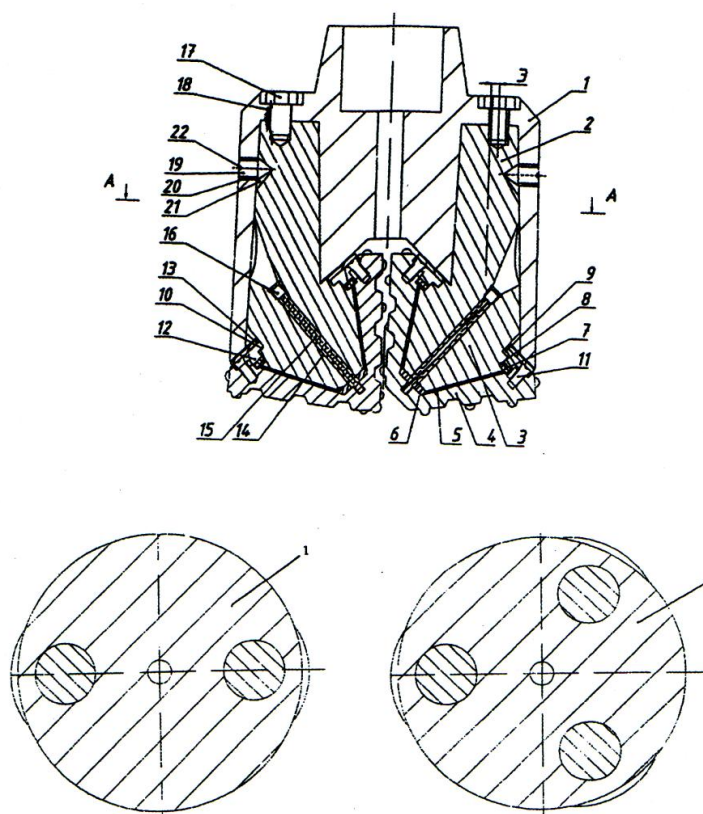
Схема разборного шарошечного долота с корпусом многократного использования, опорами скольжения и фланцевым замковым соединением (конструкции ГУЦМиЗ): 1 – корпус; 2 – хвостовик; 3 – цапфа; 4 – шарошка; 5 – плавающая втулка; 6 – упорный подшипник скольжения; 7 – уплотнительные элементы; 8 – кольцевые канавки; 9 – неразрезной накидной фланец; 10 – упорный бурт цапфы; 11 – крепежные элементы; 12 – цилиндрический выступ фланца; 13 – шайба; 14 – резервуар для масла; 15 – гибкий шнек; 16 – резьбовая пробка; 17 - крепежный болт; 18 – крепежное отверстие; 19 – выточка под ключ; 20 - крепежное отверстие; 21 – выточка под болт; 21 – болт
